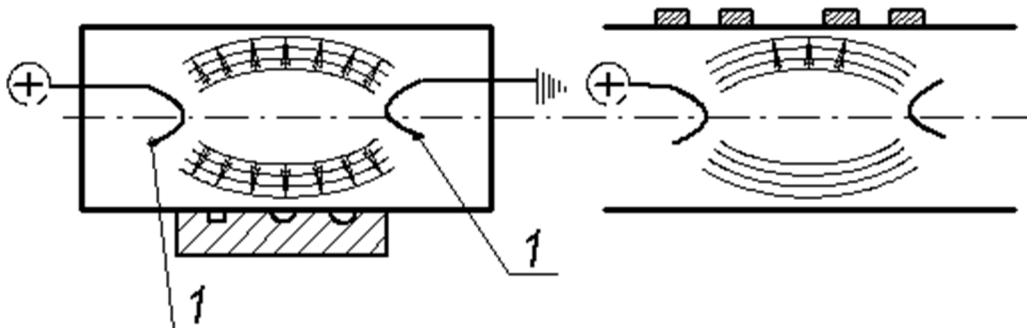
Схеми електроімпульсного отримання гофр на трубчастій заготовці та штампування плоскою заготовкою
